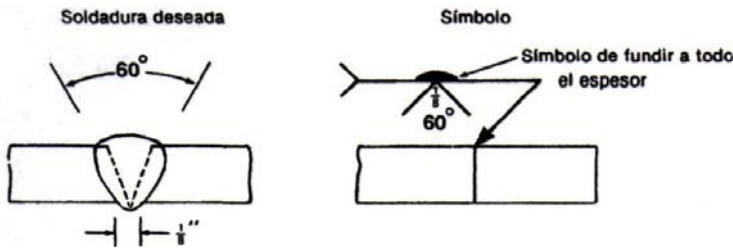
Símbolo de soldadura en el que se especifica el 100% de penetración.
